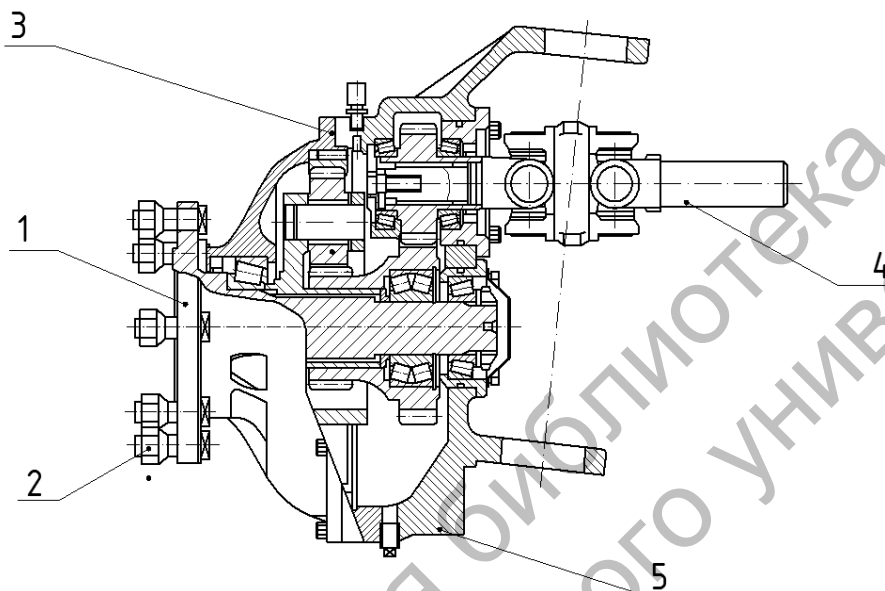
Колесная передача передних ведущих колес трактора «Беларус МТЗ-1221», не оснащенных тормозными механизмами: 1 – полуось; 2 – болт; 3 – крышка редуктора; 4 – карданная передача; 5 – корпус редуктора
